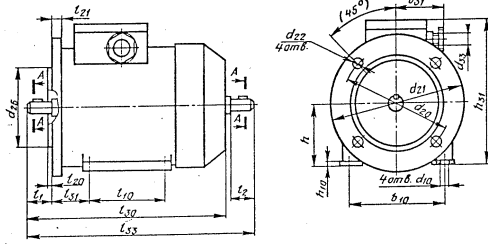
Габаритные, установочные и присоединительные размеры двигателей исполнений 1М2081, 1М2082
